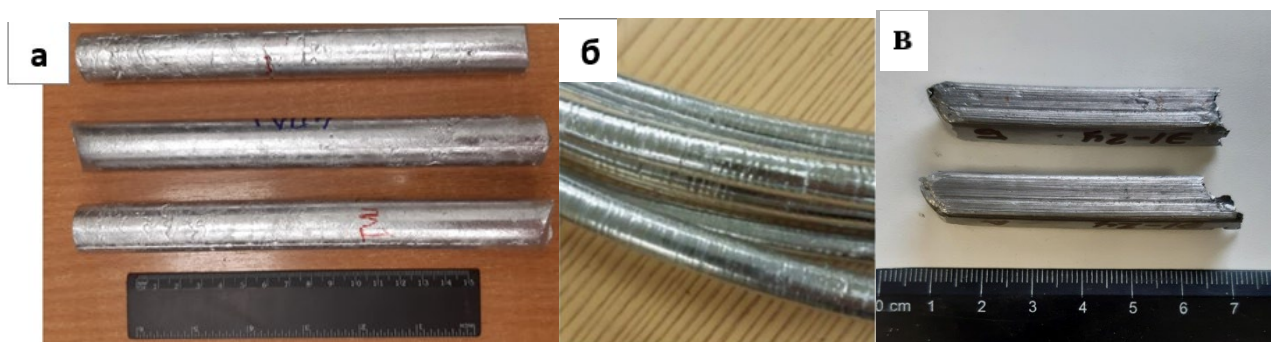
Внешний вид заготовок сплава Al-1.7Fe полученных:
